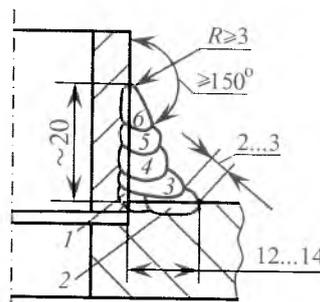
Схема расположения валиков и размеры шва приварки штуцера (трубы) из хромомолибденовой и хромомолибденованадиевой стали к коллектору (трубопроводу) без последующей термообработки по документу РД 153-34.1-003-01 (РТМ-1с): 1-6 – номера слоев
